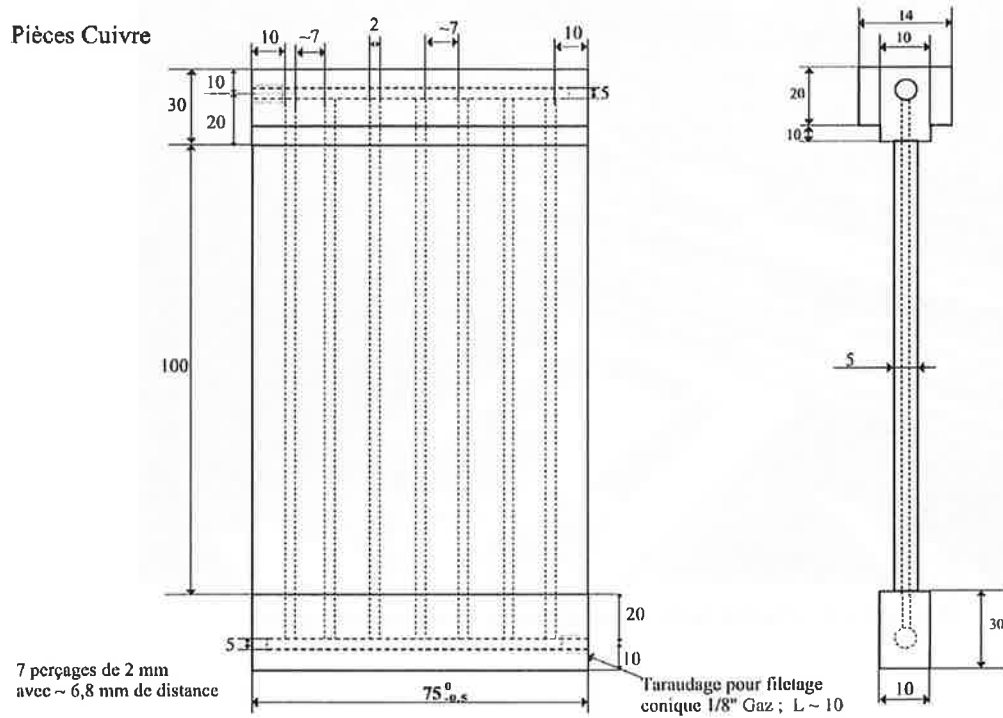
Plans des ailettes insérées dans la veine d'essais
